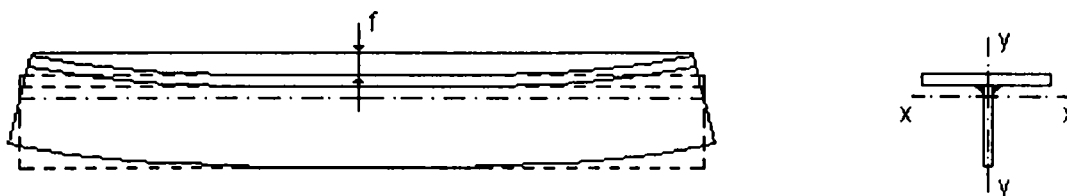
Încovoierea longitudinală a barelor cu secțiune T
